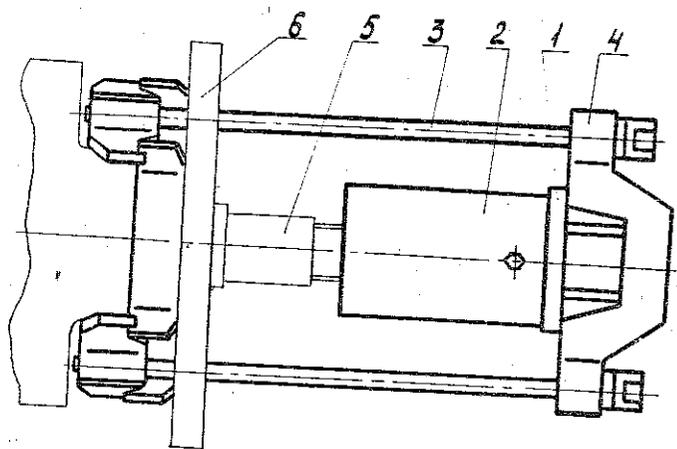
Приспособление для выемки ротора насоса БНГ-7 х 2
